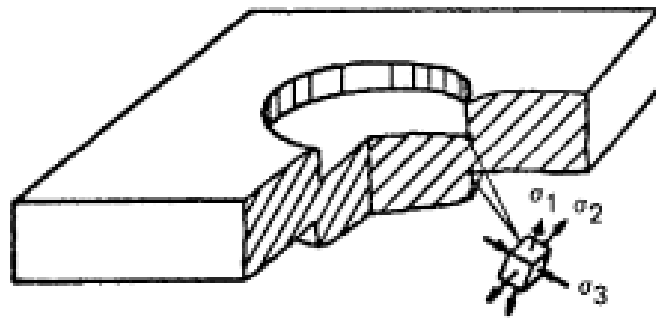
Напружений стан заготовки після чистової вирубки - пробивання.
